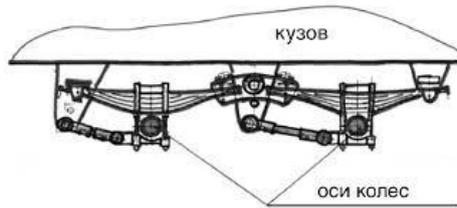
Схема двухосной тележки полуприцепа с рессорно-балансирной подвеской
